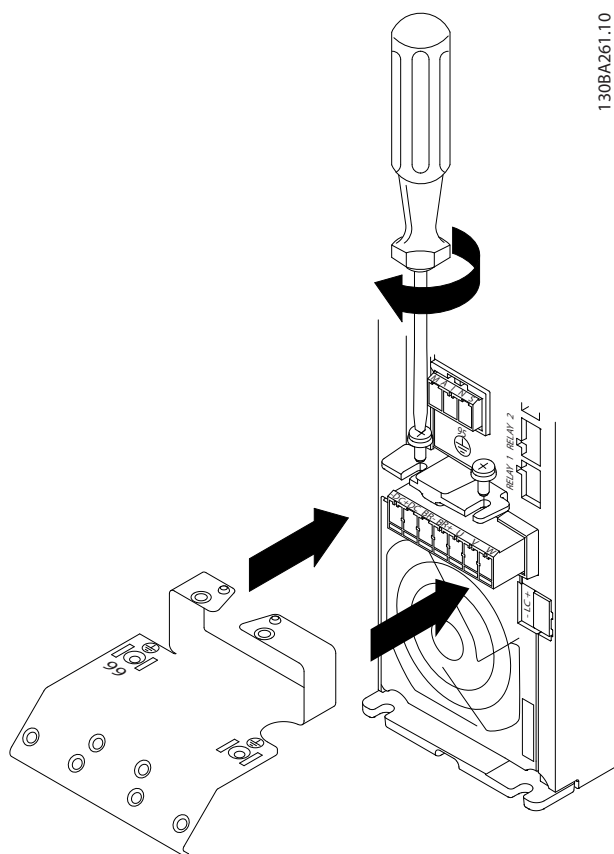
Monter les deux vis sur la plaque de montage, positionner la plaque et serrer complètement les vis
